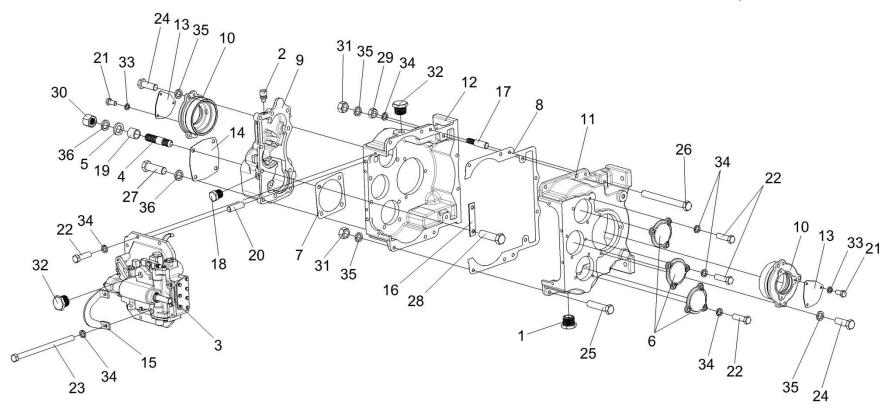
Коробка диапазонов 3518020-46150 (корпус, крышки)
